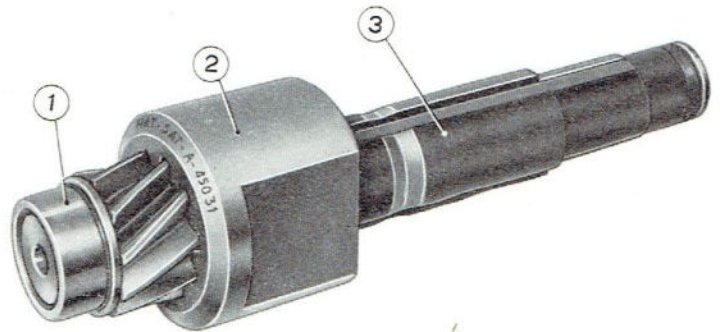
Anordnung des Werkzeugs A. 45031 zum Abziehen des Innenrings des Rollenlagers an der Motorseite von der Getriebe-Vorgelegewelle.
